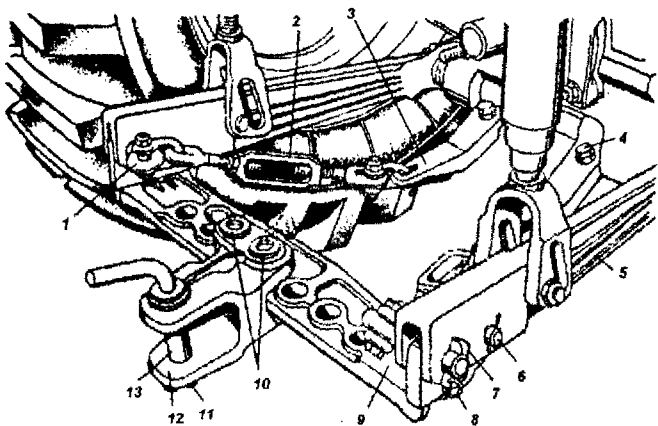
Прицепное устройство ТСУ-1-Ж в тракторах МТЗ-80, МТЗ-82: 1 - проушина; 2 - стяжка; 3 - кронштейн; 4 - регулировочный болт; 5 - продольная тяга; 6 и 10 - пальцы; 7 - чека; 8 - пружинное кольцо; 9 - поперечина; 11 - пружинный шплинт; 12 - прицепная вилка; 13 - шкворень
